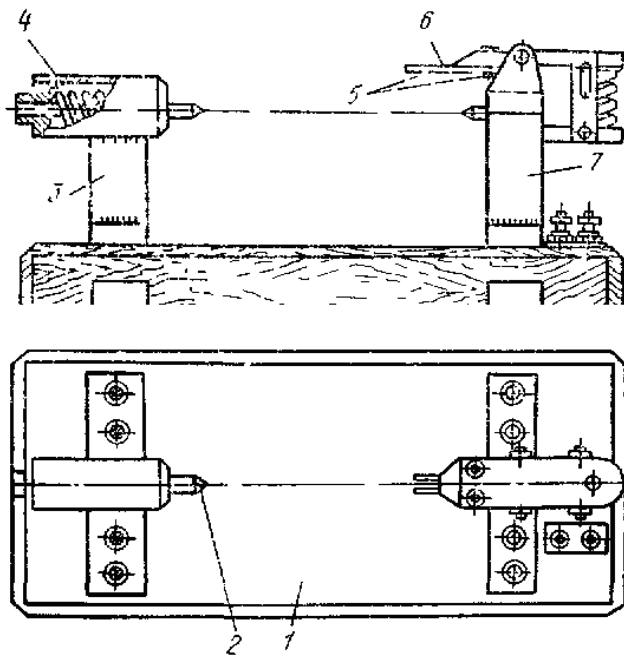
Пристрій для перевірки якоря на міжвиткове і межламельне замикання: 1 - дошка; 2 - центр; 3,7 - стійки; 4 - пружина; 5 - контакти; 6 - контактна пластина
